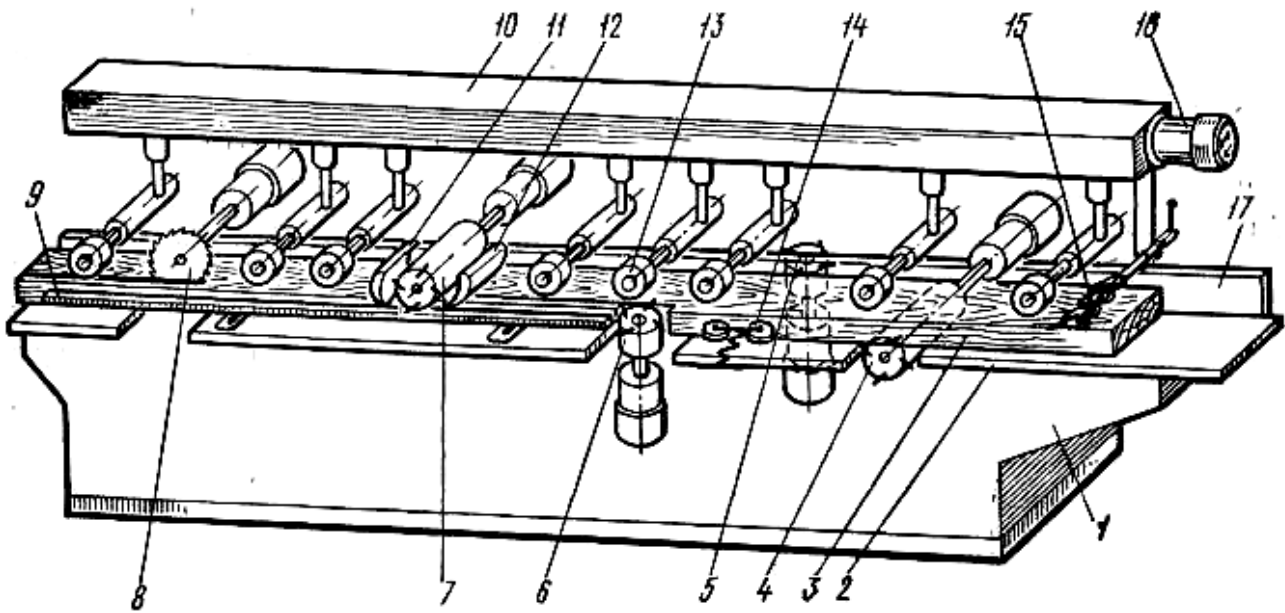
Схема четырехстороннего продольно-фрезерного станка с распределенной подачей материала:
